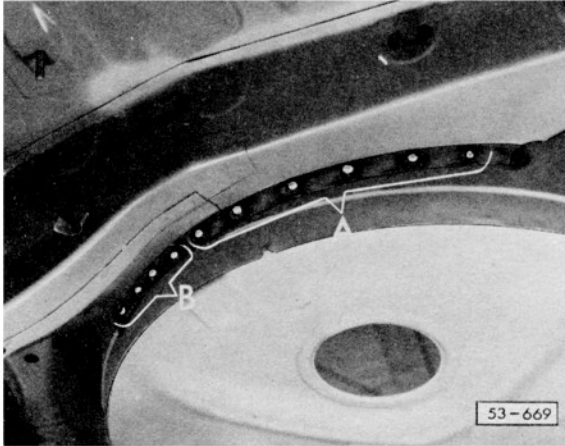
Kofferboden hinten – Teilstück einschweißen
